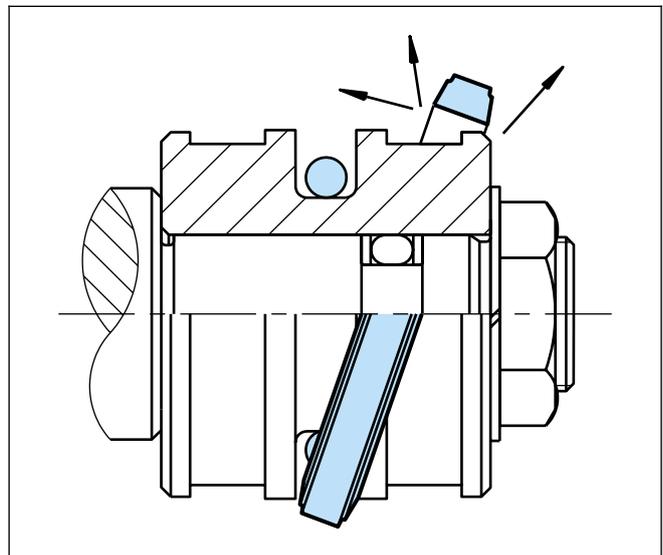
Aufziehen des Dichtringes auf den in die Nut eingelegten O-Ring
